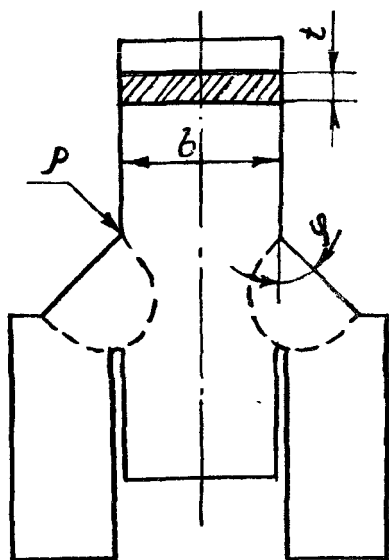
Схема нахлесточного соединения с угловыми швами
